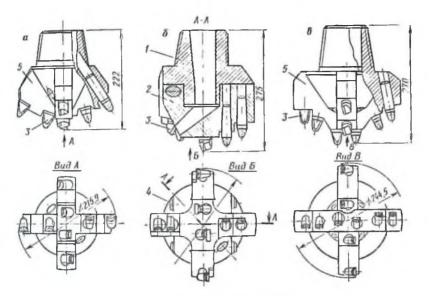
Режущие долота для бурения с продувкой: a-3РД215,9; 6-1РД244,5; 6-3РД214,5; 1-хвостовик; 2-съемвый корпус; 3-сменный резец типа ШБМ2С; 4-звыковый палец; 5-корпус долота
